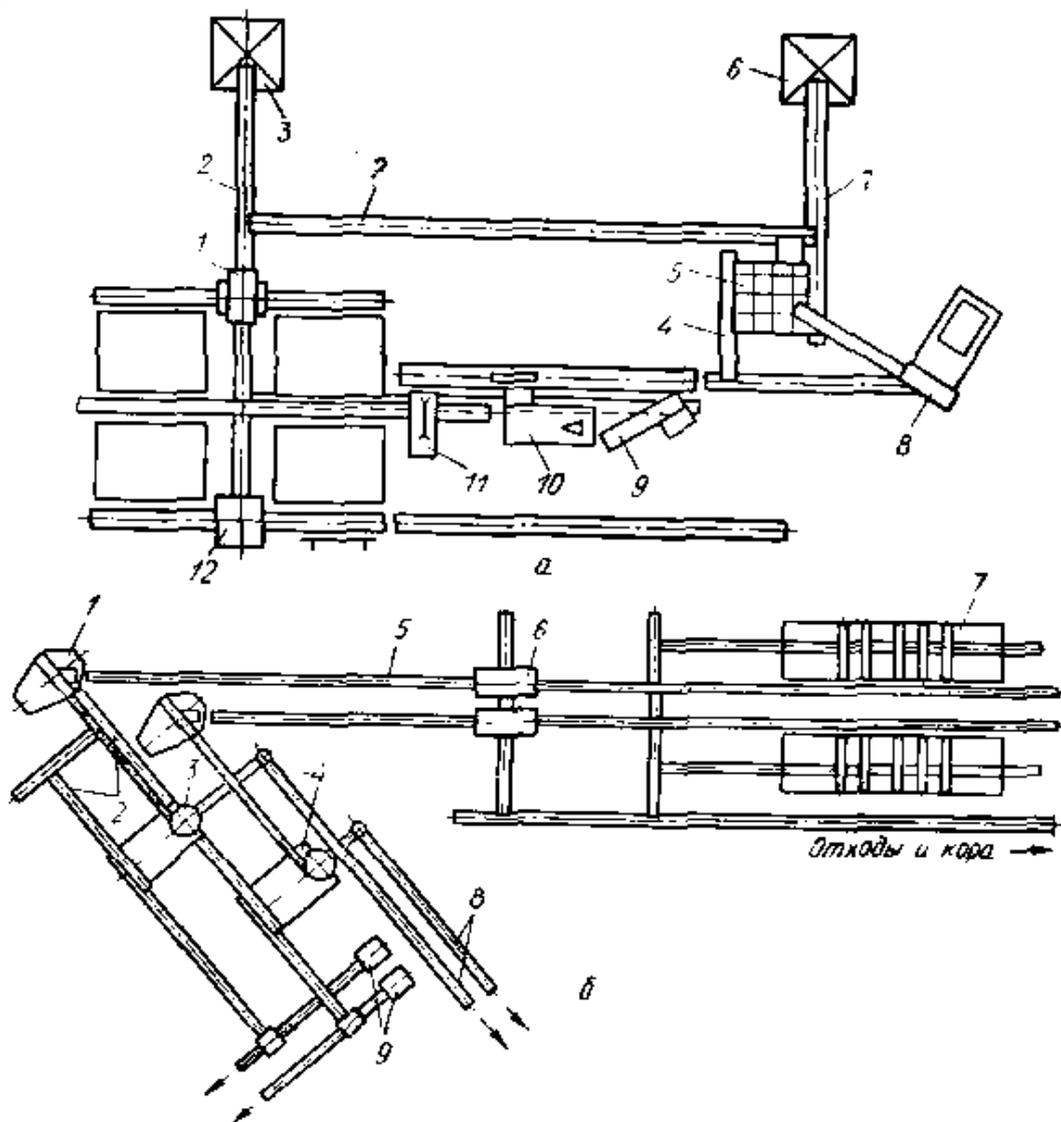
Схема цеха щепы на базе роторных окорочных станков
